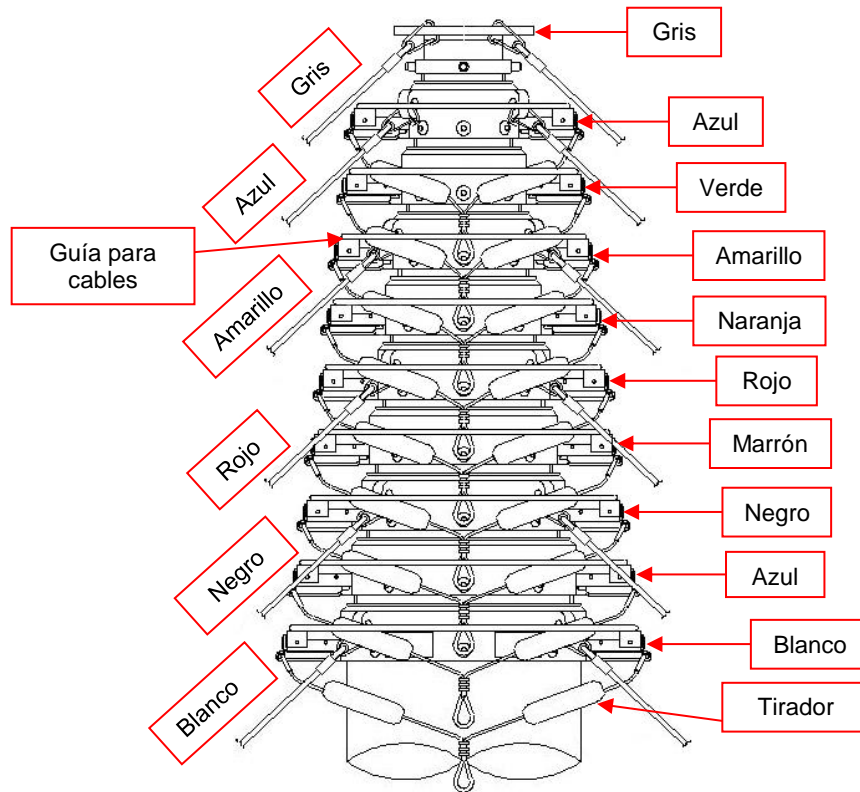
Muestra de montaje en un mástil con Guías para Cables (Mostrado Mástil con eslingas con guardacabos)
